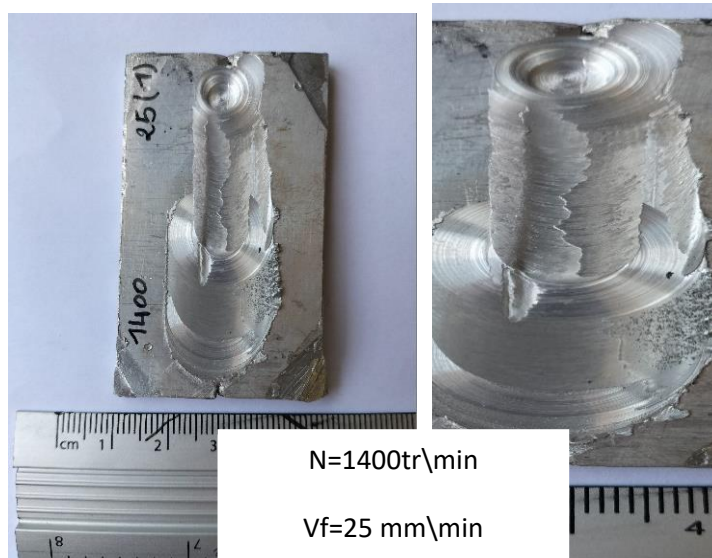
Eprouvette soudée par soudage friction malaxage.
